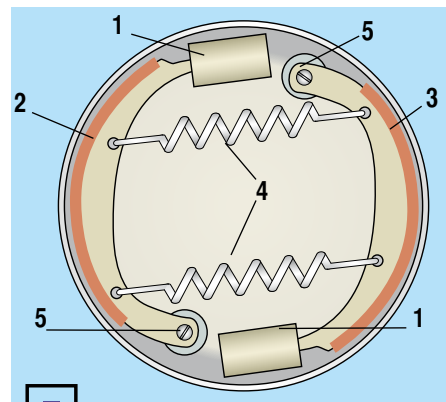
Механизм с разнесенными опорами колодок: 1 – колесный цилиндр; 2 – накладка передняя; 3 – накладка задняя; 4 – стяжная пружина; 5 – узел шарнирного крепления колодок
